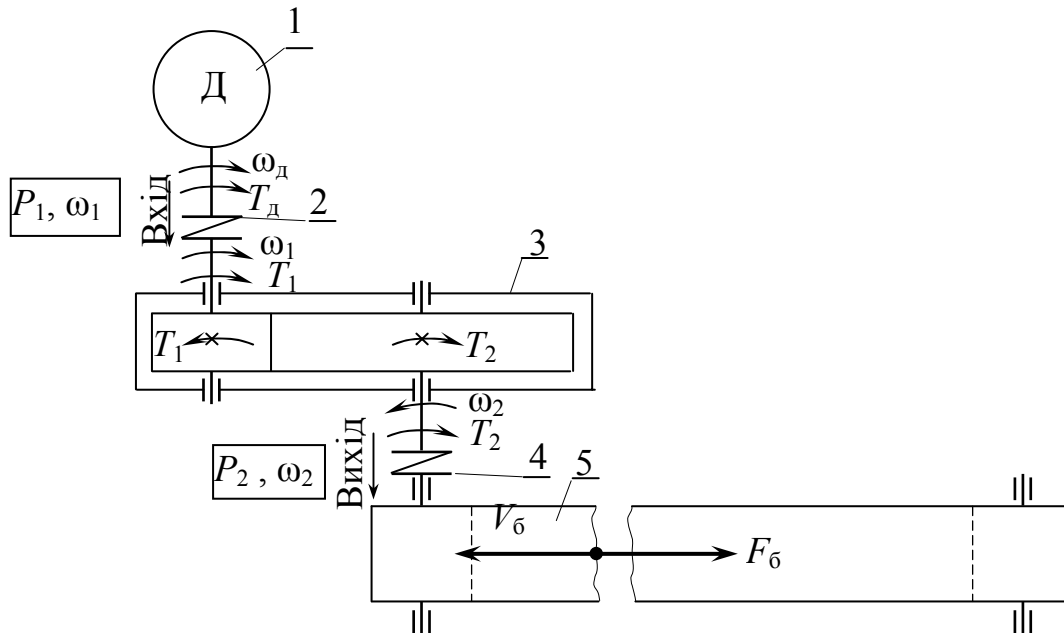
Кінематична схема приводу стрічкового конвеєра : 1 – електродвигун ; 2, 4 – муфти; 3 – зубчастий редуктор; 5 – стрічковий конвеєр
